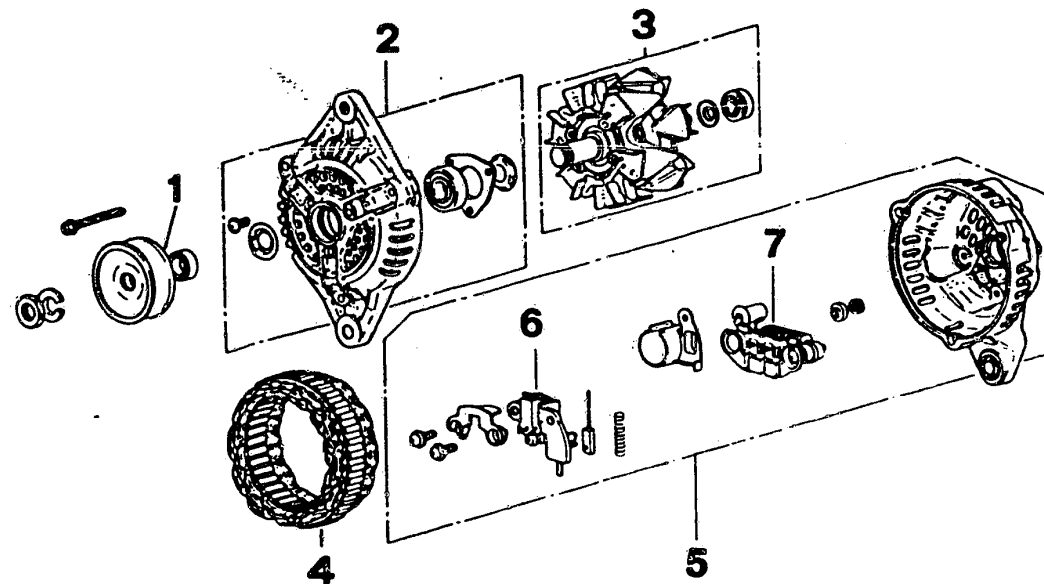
Einzelteile des Generators: 1 Riemenscheibe – 2 vorderes Gehäuse-teil mit Lager – 3 Rotor mit hinterem Lager und Ventilator – 4 Stator – 5 Hinteres Gehäuse-teil – 6 Kohlen mit Halterung – 7 Dioden mit Träger.
